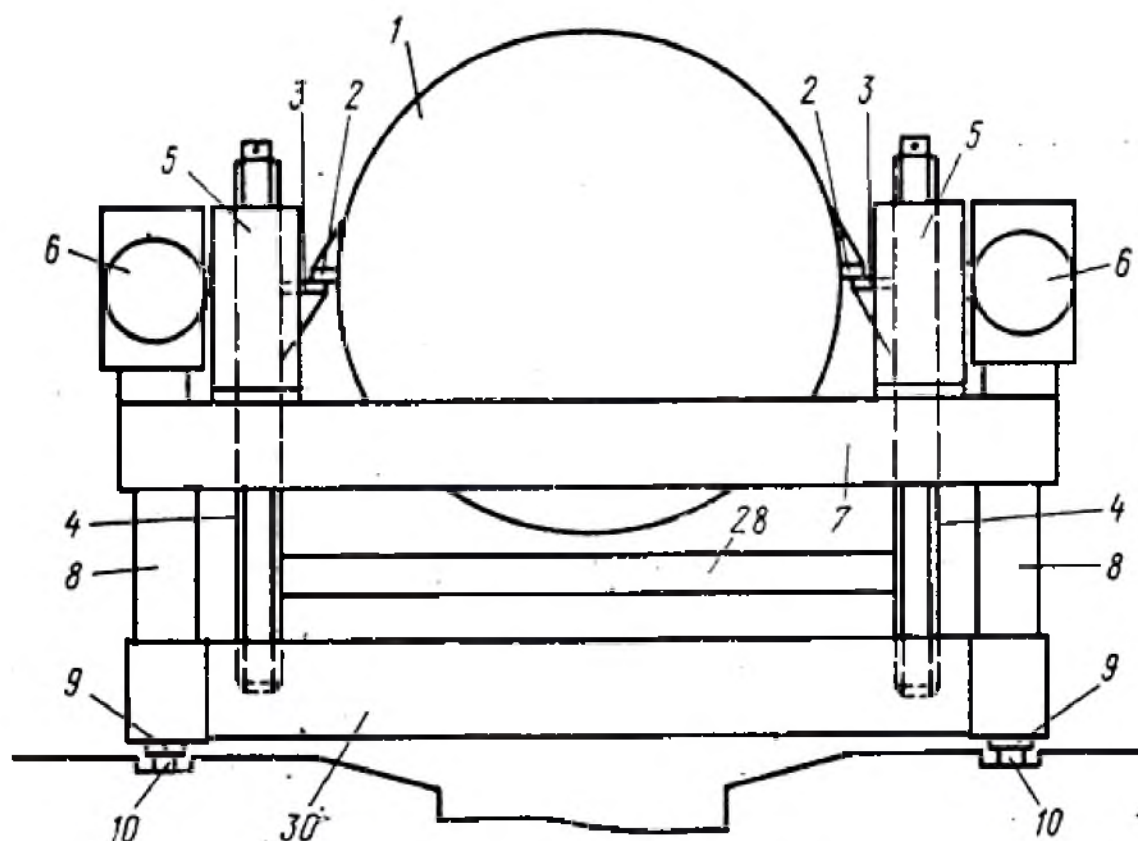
Пристрій для розливання металу (вид ззаду)
